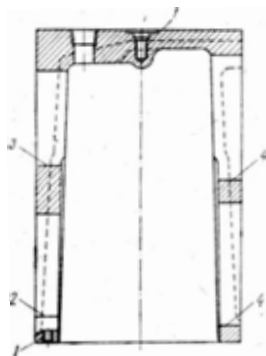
Корпус редуктора ВВП 150.41.101-4. Схема дефектів
